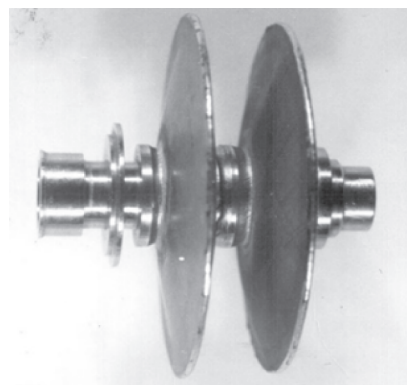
Штампованный фильтр из стали 12X18H10T, обеспечивающий тонкость очистки 10...12 мкм
